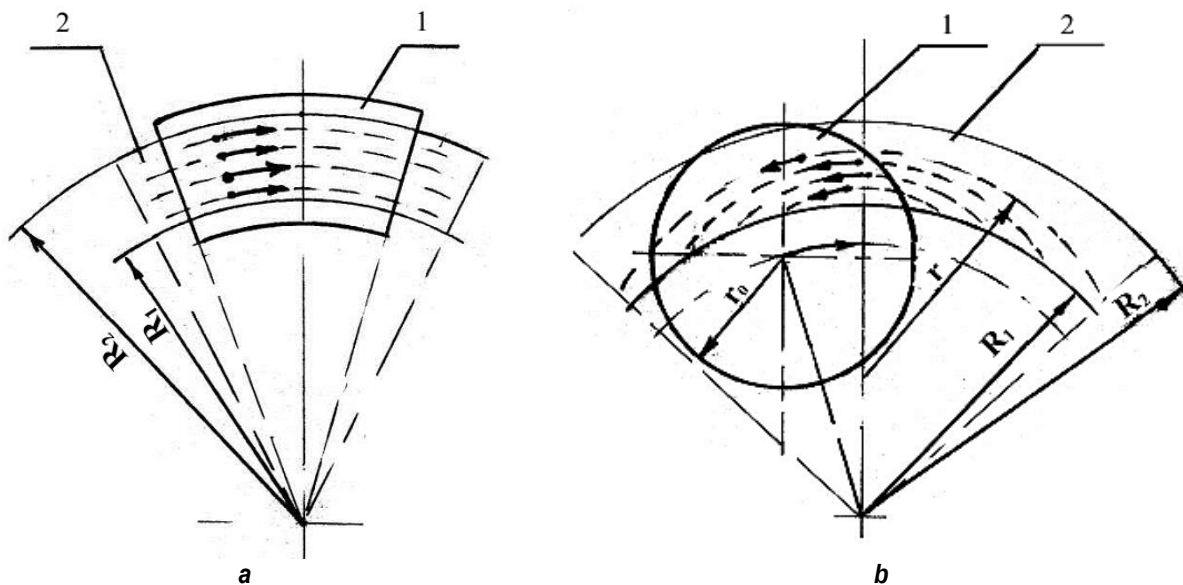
Кинематика обработки деталей-свидетелей одно- (а) и многодисковыми (б) шлифовальными головками
